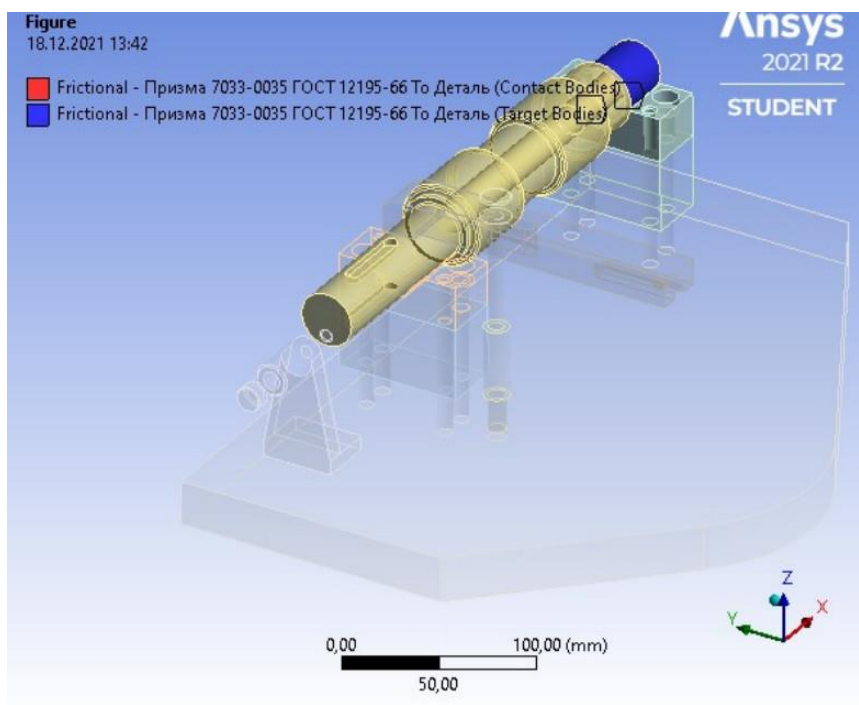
Сполучення між поверхнею заготовки та задньою призмою
